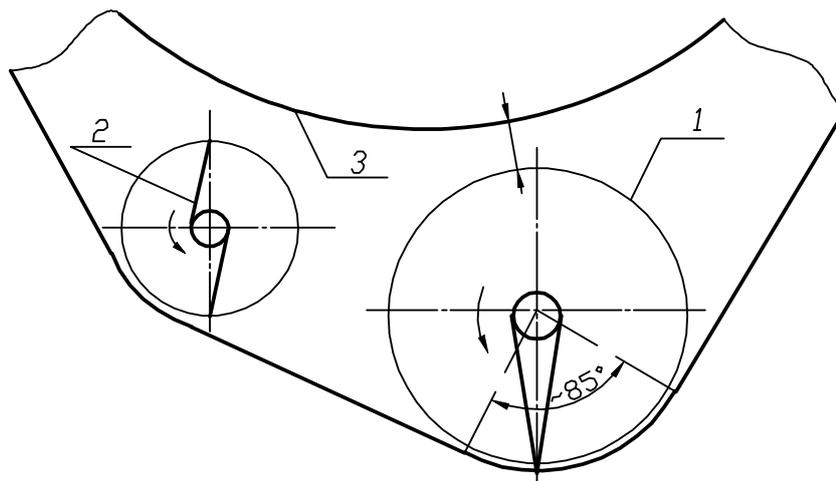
Схема шнеко-битерного устройства: 1 – шнек; 2 – битер; 3 – кожух ротора
